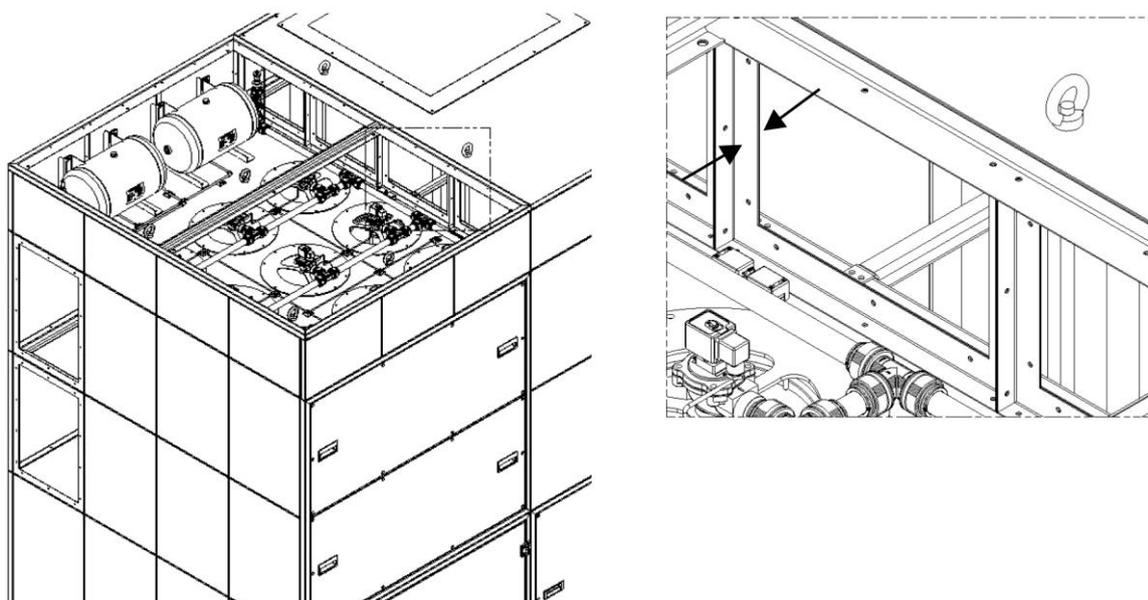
raccordement de la section du ventilateur à la section du filtre
